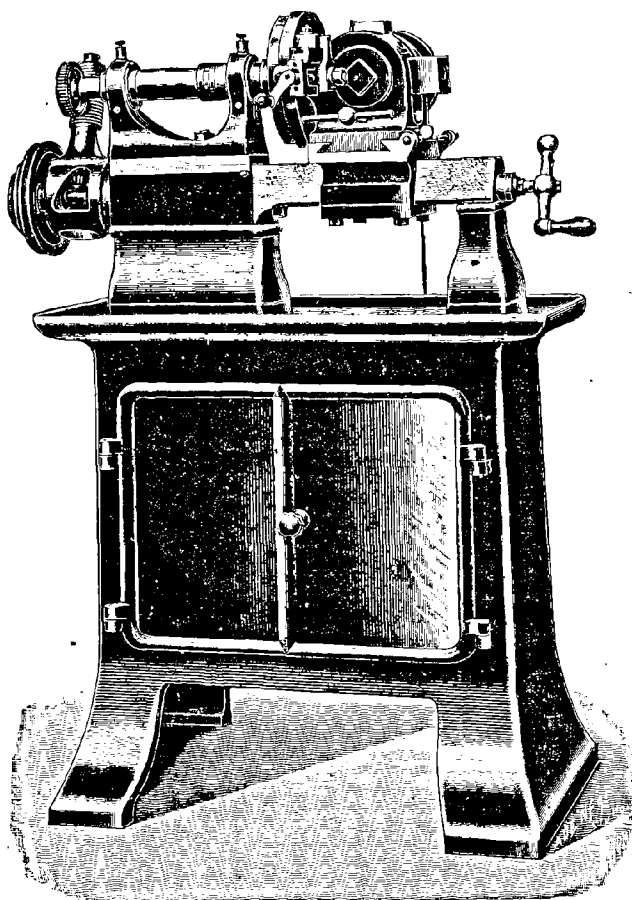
Machine automatique du « Progrès Industriel » pour la reproduction des cames plates.
